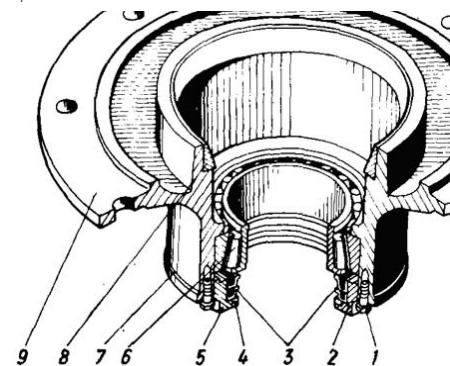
Разборка картера: 1 — болт; 2 — шайба; 3 — манжета; 4 — кольцо; 5 — крышка; 6 — подшипник; 7 — прокладка; 8 — обойма наружная подшипника; 9 — картер
